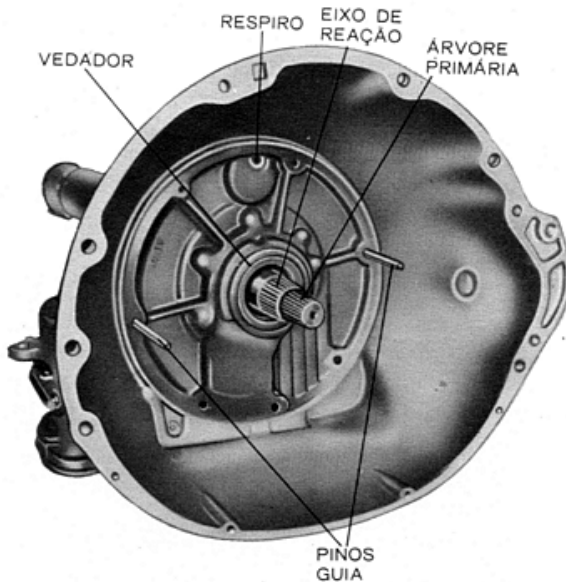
Instalação do conjunto da bomba de óleo e suporte do eixo de reação
